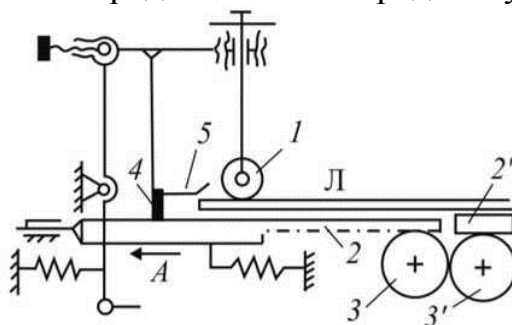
Схема механизма бокового выстойного выравнивания: 1 - обрезиненный ролик; 2 - подвижная планка; 3 - зубчатый привод планки; 4 - упор; 5 - приклон-козырек; Л - лист
